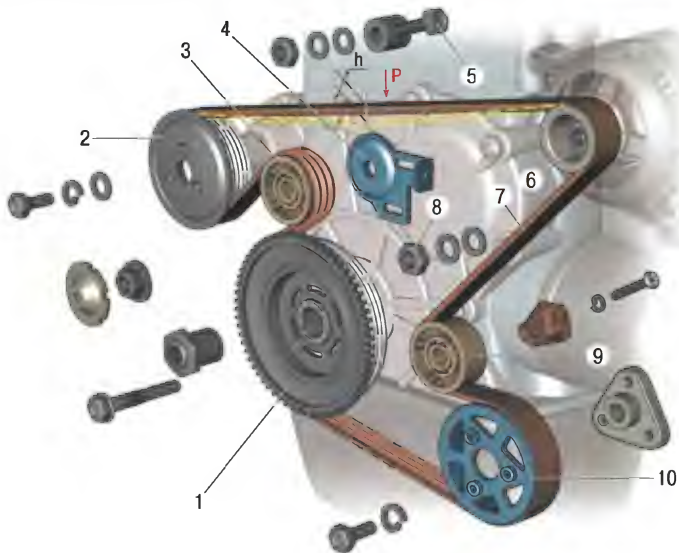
Схема проверки натяжения ремня привода генератора
